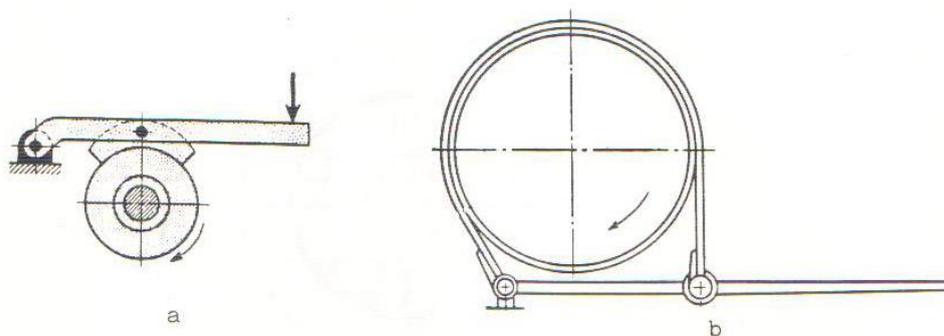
Freio de sapata externa (a); de cinta sobre tambor (b)
